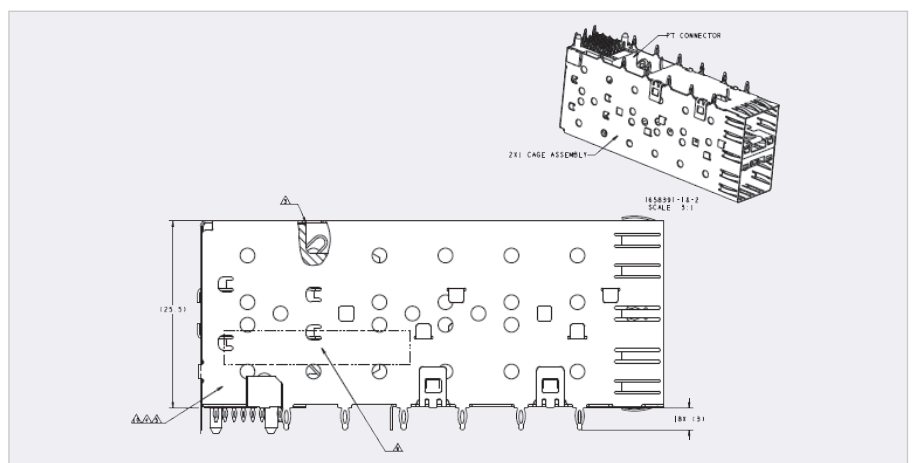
Фрагмент чертежа на разъём SFP & Cage Connector 1658391-1. Сноски на п. 4 и п. 10 ТТ чертежа касательно материала штырей Cage заключены в значки треугольников в левой части чертежа со стрелкой
